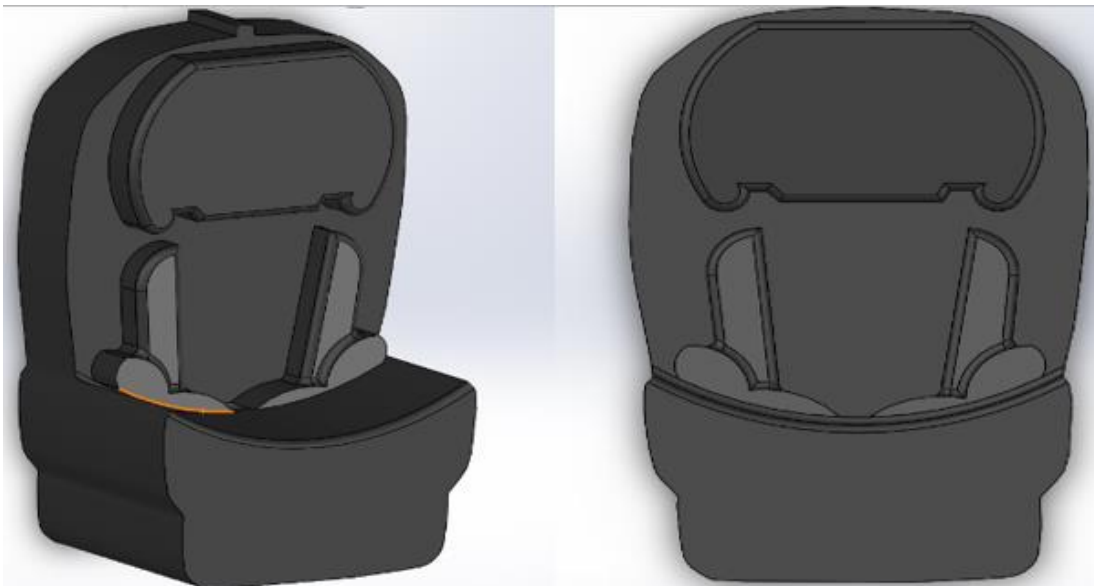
Diseño de la silla en SolidWorks (propia autoría)
